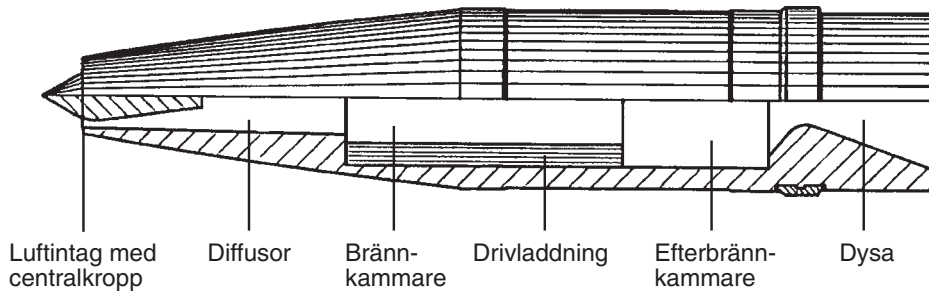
SFRJ – Solid Fuel Ramjet-motor
